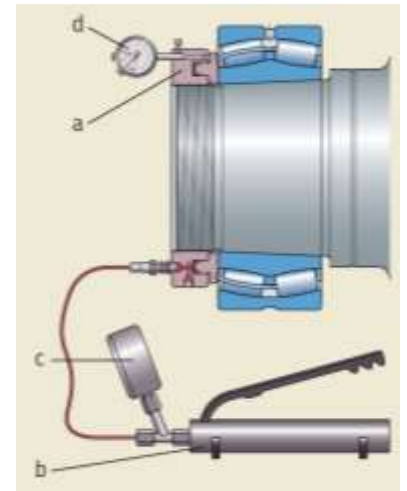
Монтаж підшипника методом SKF Drive-up.
